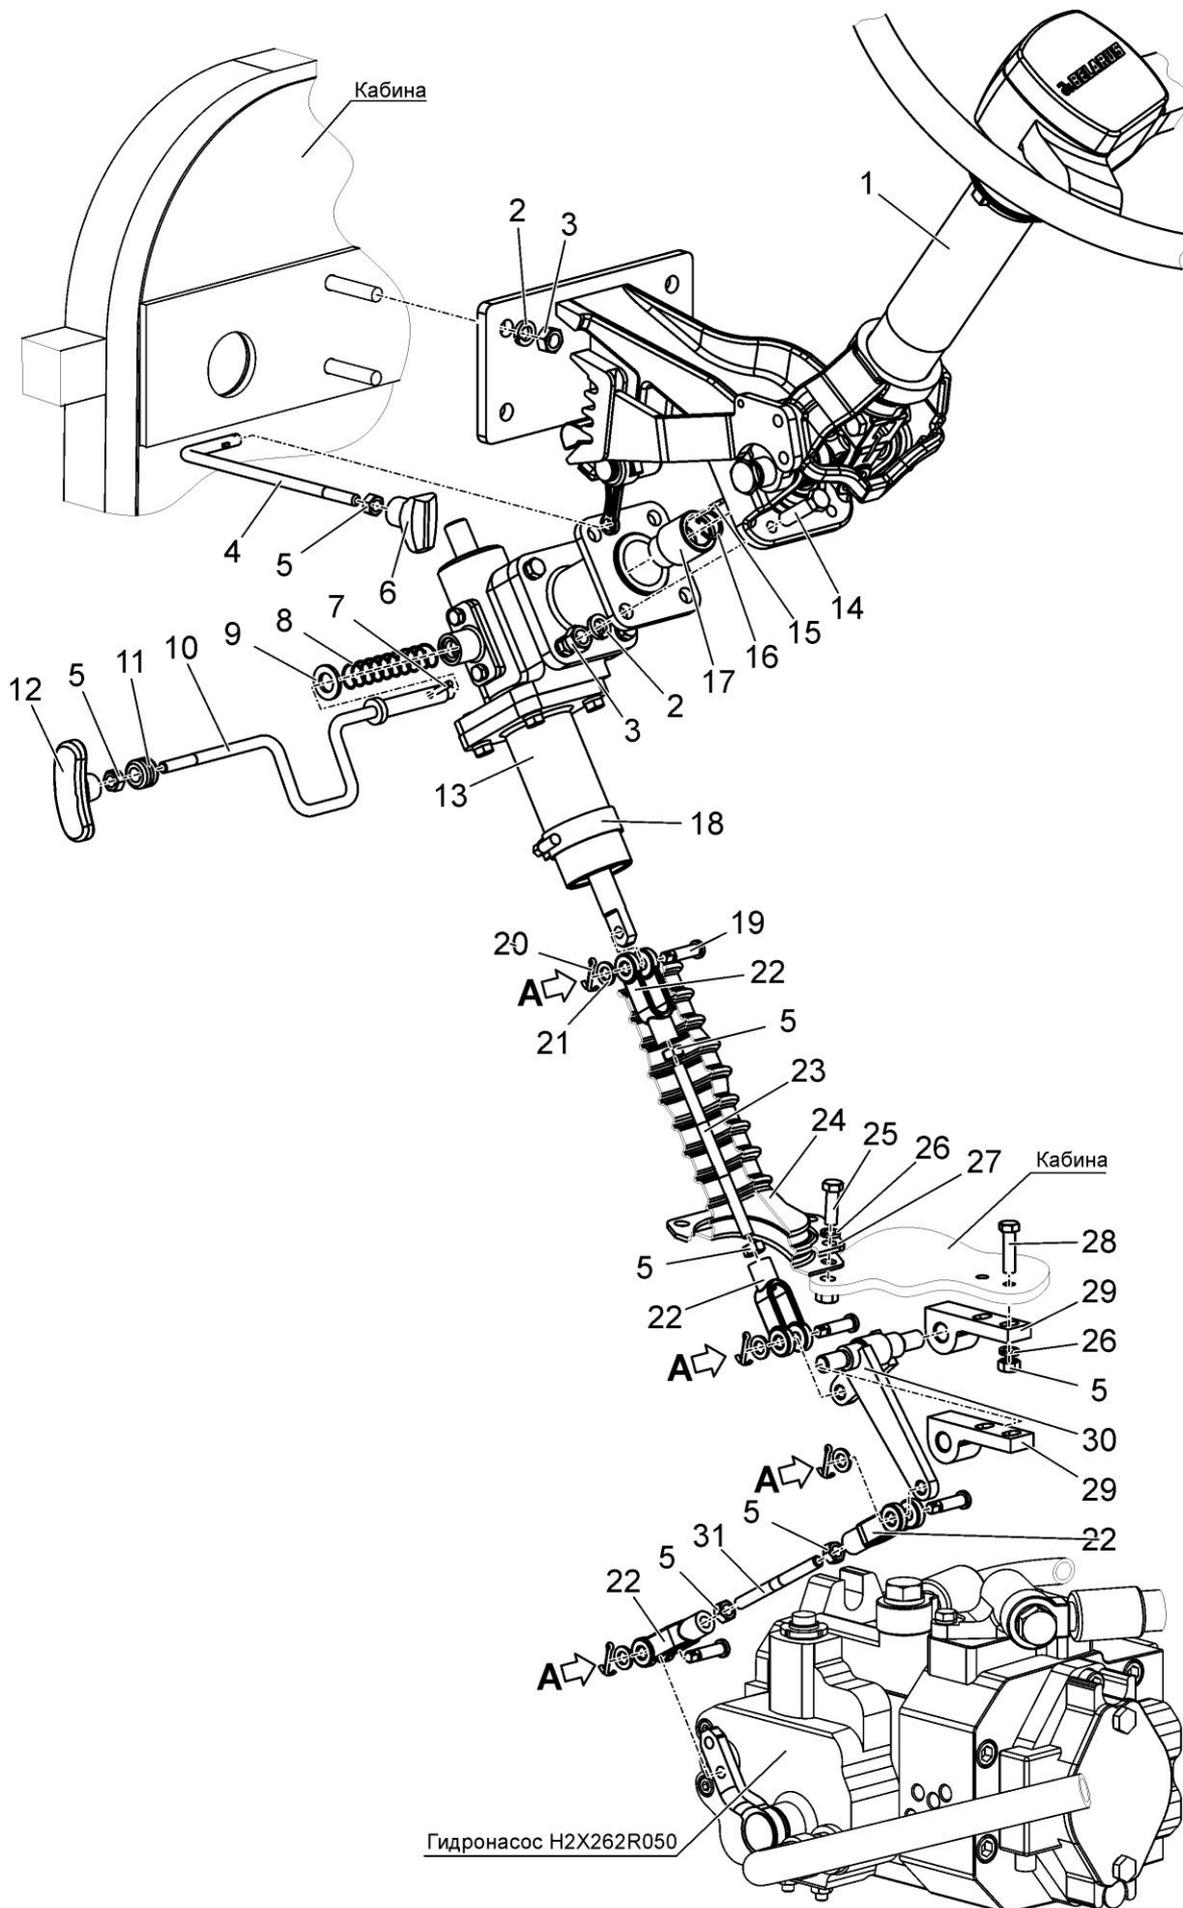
Привод поворота рулевой. Колонка рулевая. Тяга
